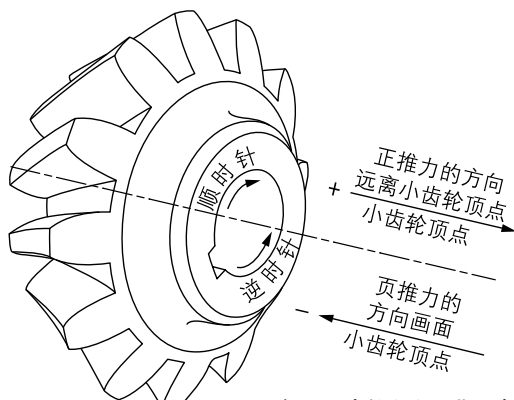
螺旋锥齿轮和准双曲面齿轮传动—推力和分离力的方向取决于螺旋角度、螺旋螺旋线方向、旋转方向以及齿轮是主动齿轮还是从动齿轮
